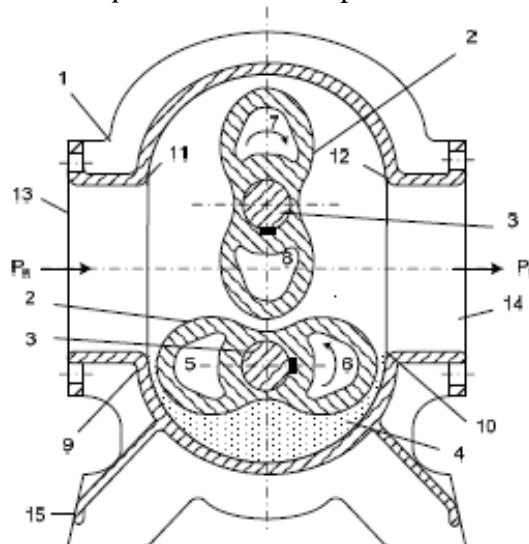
Secțiunea printr-un compresor cu lobi:
